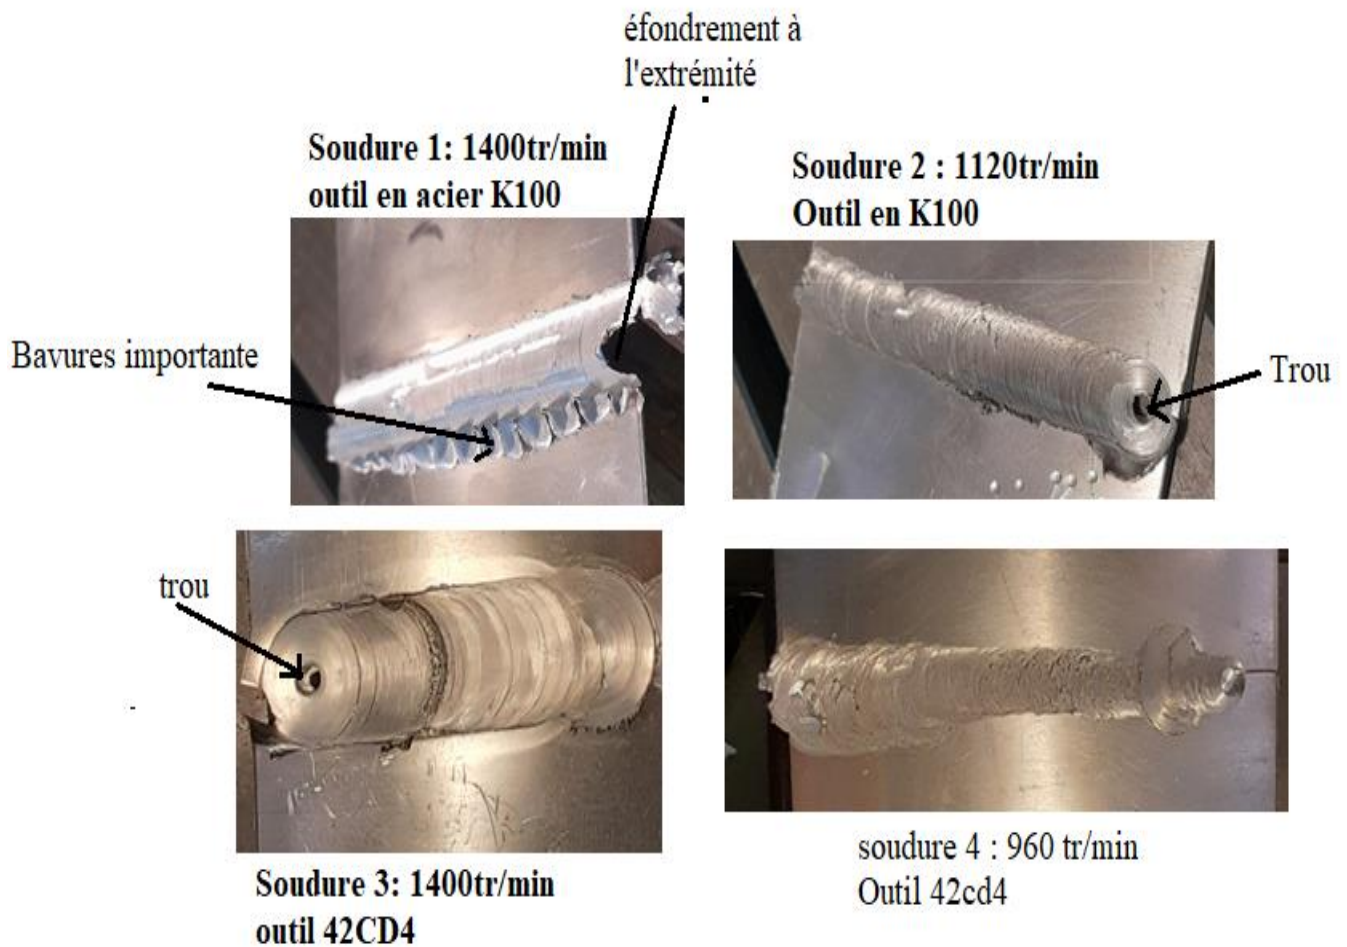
Photographies des cordons de soudures FSW obtenus
